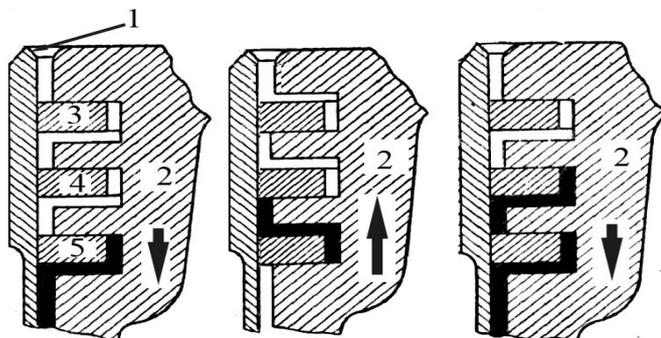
Схема насосного действия поршневых колец. Обозначения: 1 – стенка цилиндра, 2 – поршень, 3...5 – поршневые кольца. Стрелкой указано направление движения поршня
